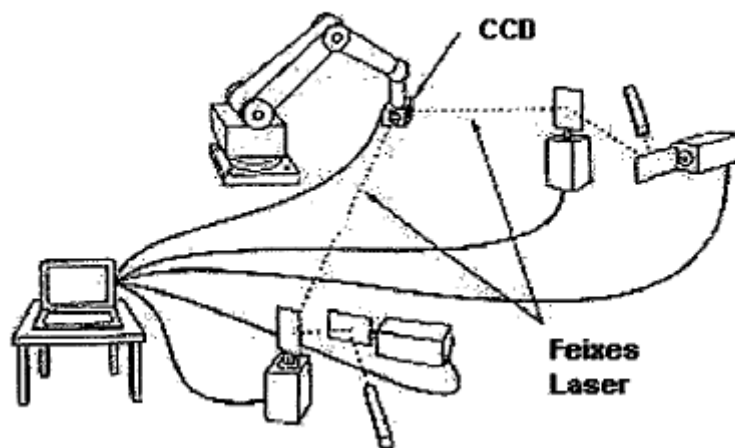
laser tracking e sensor CCD (traduzida de [27])
